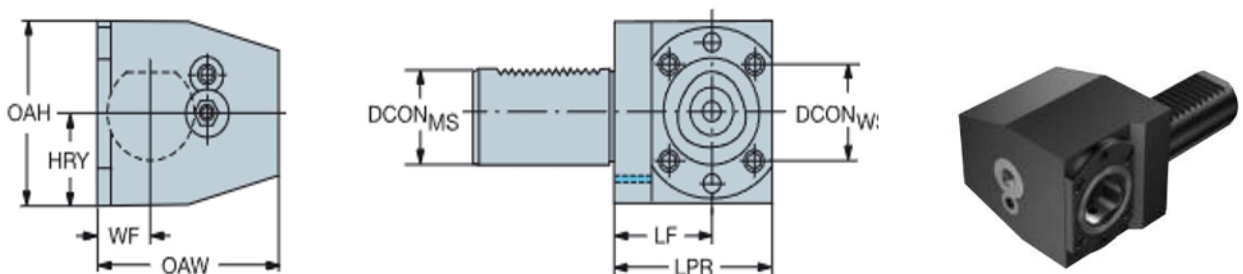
Інструментальний блок марки Coromant Capto C4-R/L-C2040-51030M [3, с. E6]
